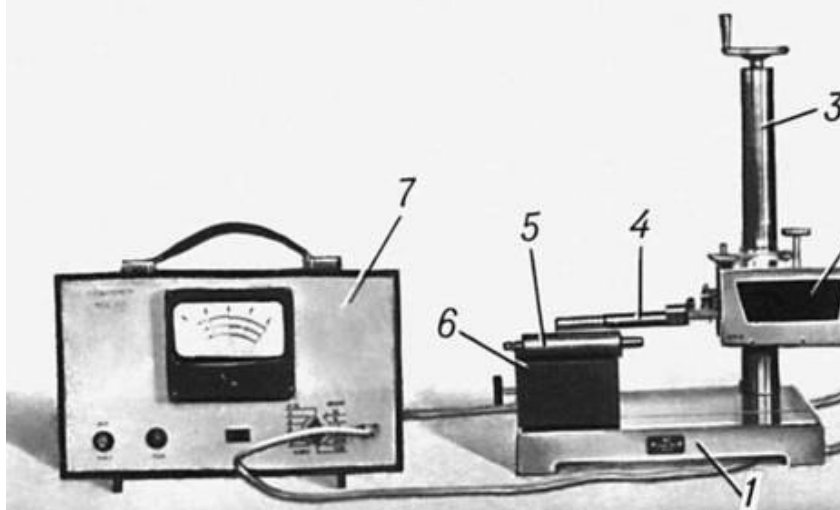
Профилометр (модель 253) 1 — станина; 2 — привод; 3 — стойка; 4 — датчик; 5 — деталь; 6 — измерительный столик; 7 — электронный блок с показывающим устройством.
